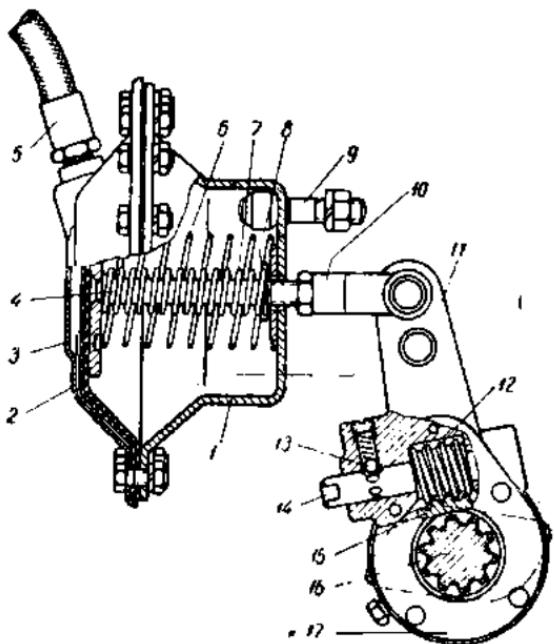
Тормозная камера. (1 — корпус камеры; 2 — диафрагма; 3 — крышка; 4 — шток; 5 — шланг подвода воздуха; 6 и 7 — пружины; 10 — вилка штока; 11 — рычаг привода тормоза; 12 — регулировочный винт; 13 — фиксатор; 14 — вал регулировочного винта; 15 — винтовое колесо; 16 — вал разжимного кулака; 17 — корпус).
